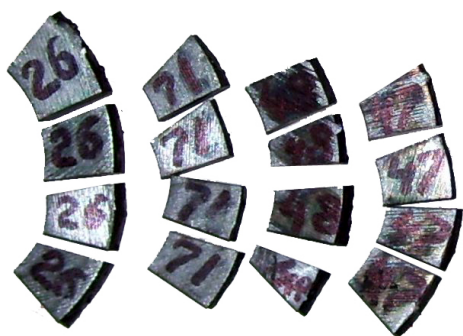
Внешний вид образцов, вырезанных из наплавленных цилиндрических заготовок
